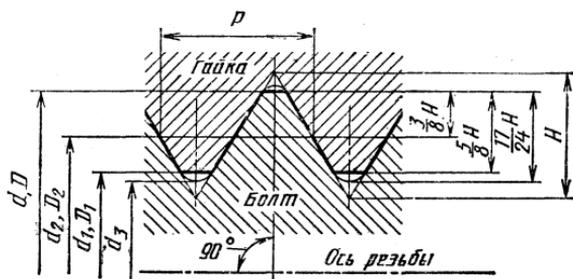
Основные элементы метрической резьбы общего назначения (ГОСТ 24705—81);
